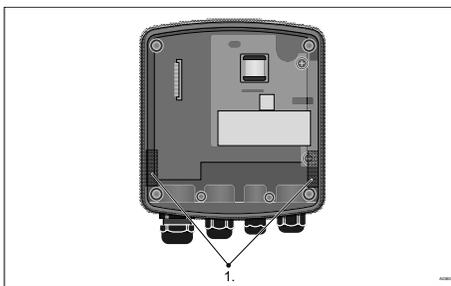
Установка профильного уплотнения на нижнюю часть корпуса регулятора
